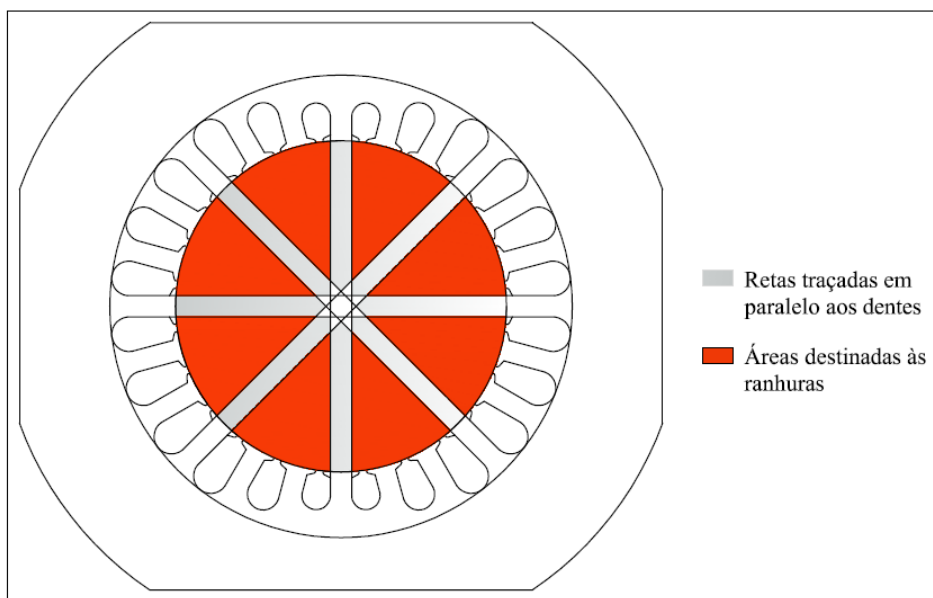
Definição do número de ranhuras do novo dispositivo.
